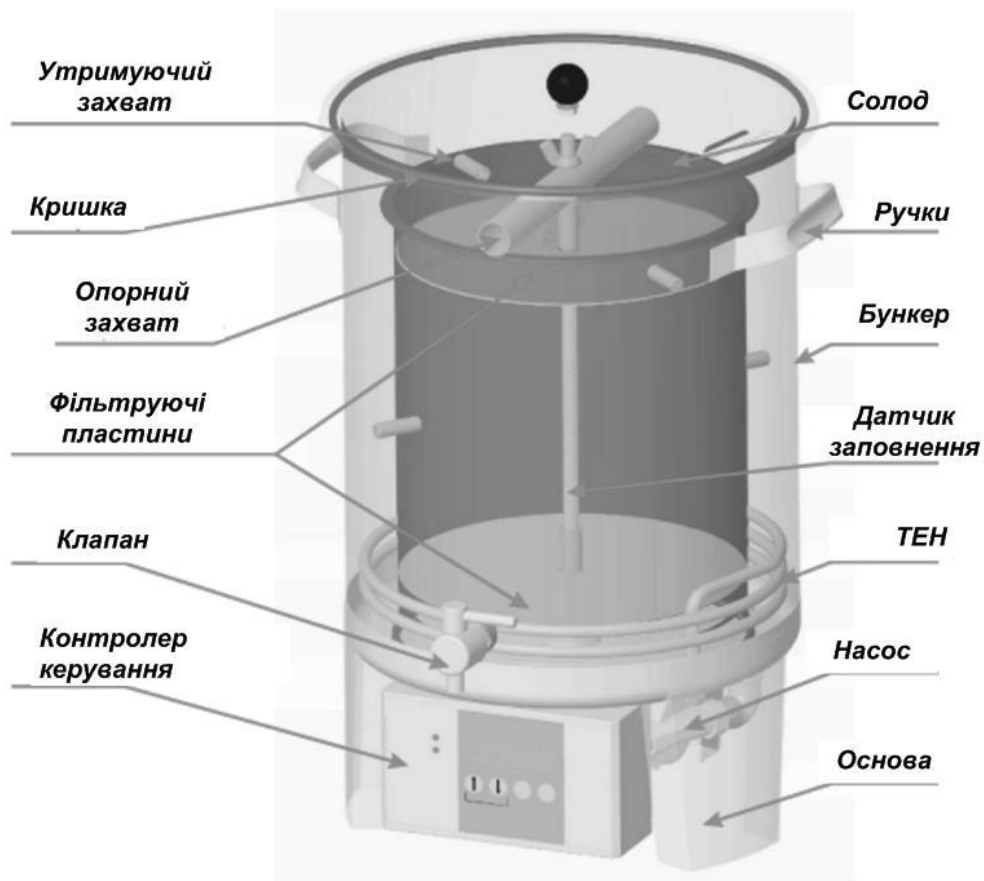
Основні частини портативного агрегату для виготовлення пива
